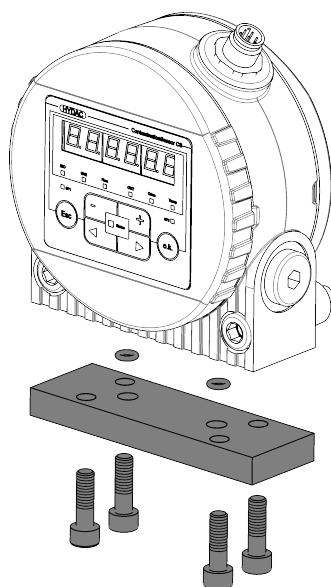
Montaggio su piastra di collegamento con attacco a flangia
